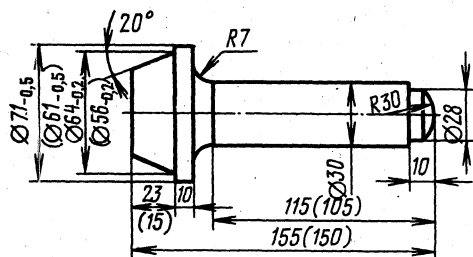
Оправка для запрессовки наружного кольца заднего подшипника ведущей шестерни главной передачи в картер редуктора автомобиля «Москвич» (в скобках — размеры для кольца переднего подшипника)
